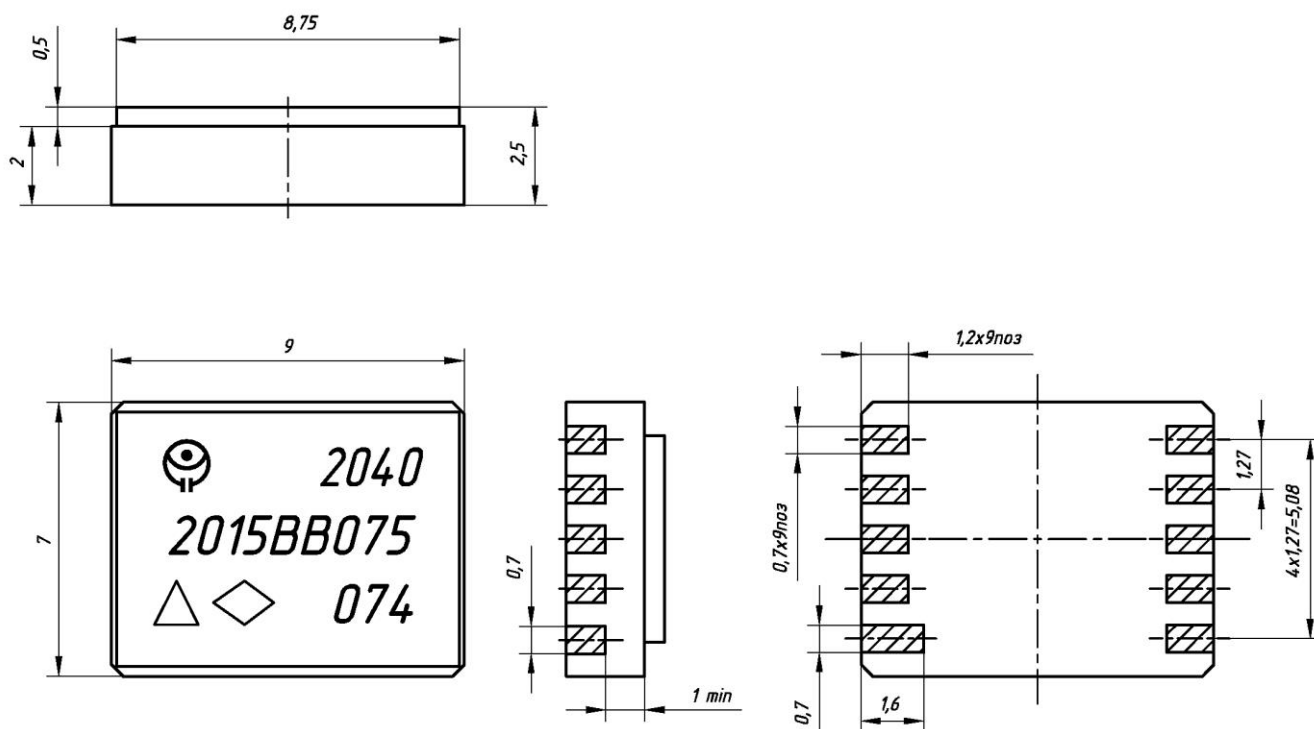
Габаритный чертеж микросхемы 2015BB075 в корпусе МК 5232.10-А
